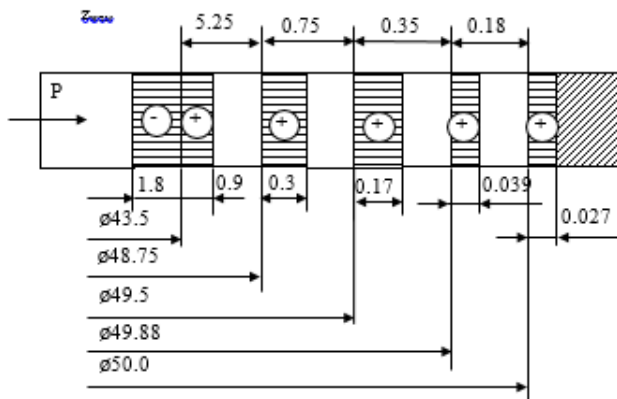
Графическая схема расположения припусков и допусков на обработку отверстия зубчатого колеса
